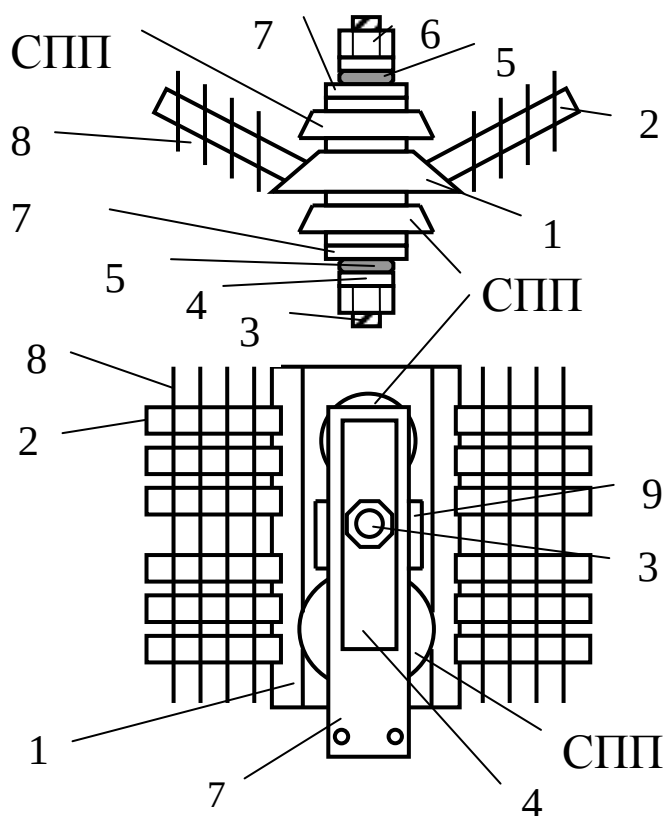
Компоновка СПП с охладителем: 1 – испаритель ДТС (охлаждаемая шина); 2 – трубчатый конденсатор ДТС; 3 – центральная стяжная шпилька; 4 – траверсы; 5 – стандартный электроизолятор; 6 – гайки стяжного устройства; 7 – токоведущая шина; 8 – пластинчатое оребрение конденсатора; 9 – прямоугольное отверстие в корпусе испарителя для установки стяжной шпильки.
